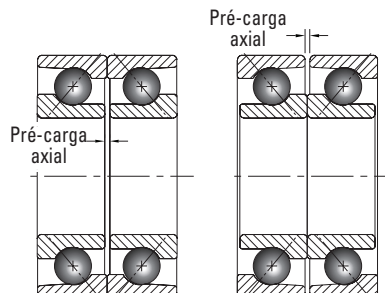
Pré-carga axial para rolamentos universalmente combinados.
